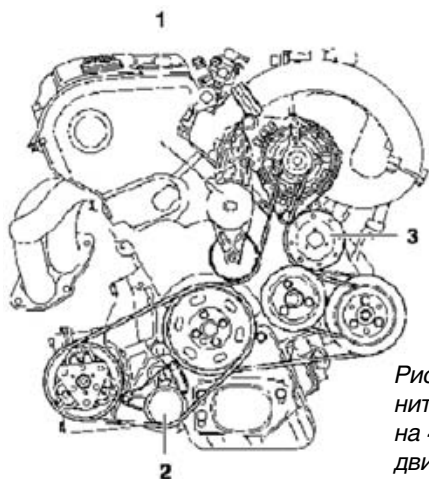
Привод дополнительных агрегатов на 4-цилиндровом двигателе.
